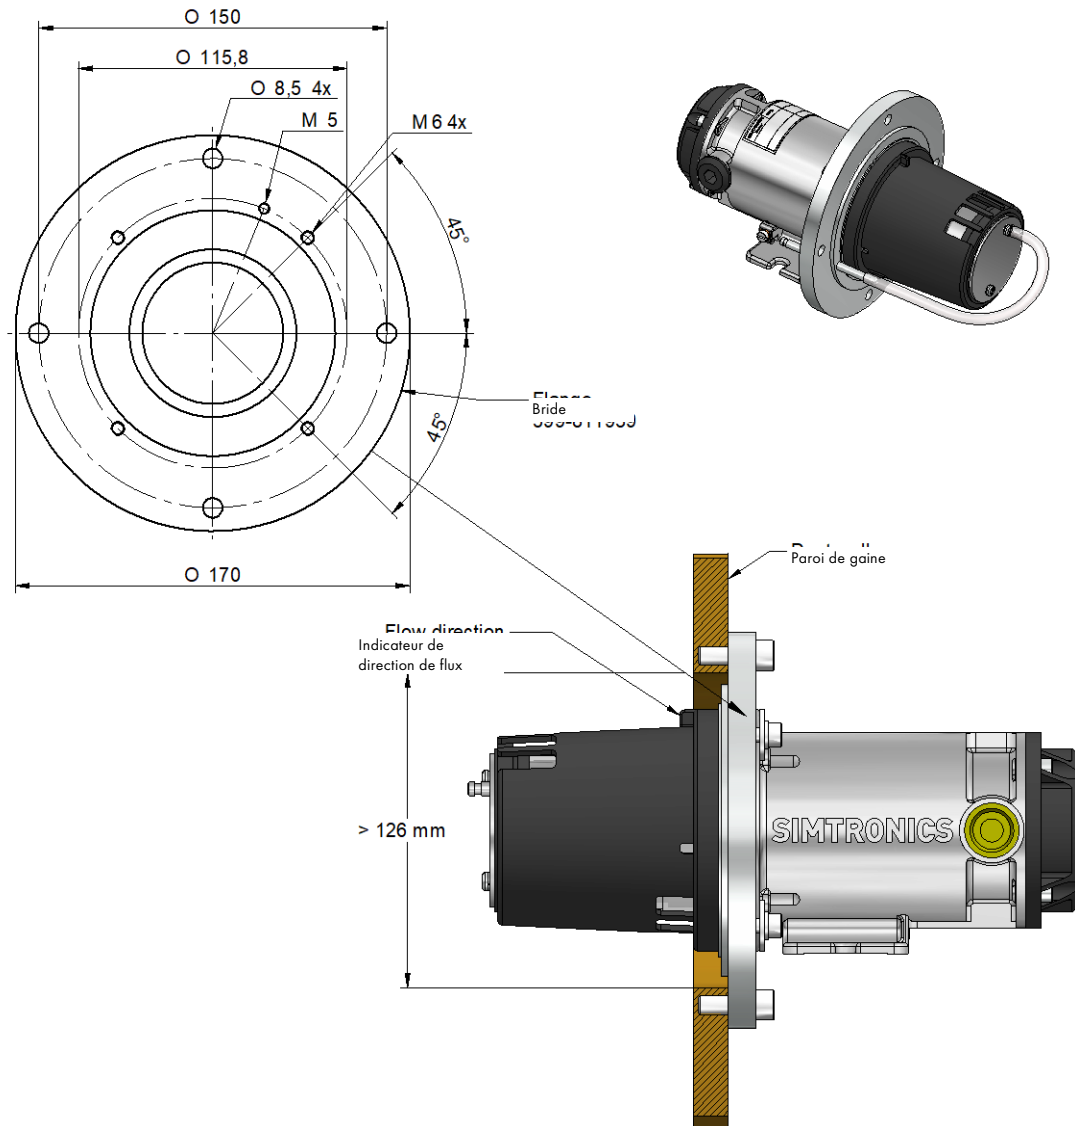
Montage sur gaine ou conduit de ventilation avec kit de montage sur gaine
